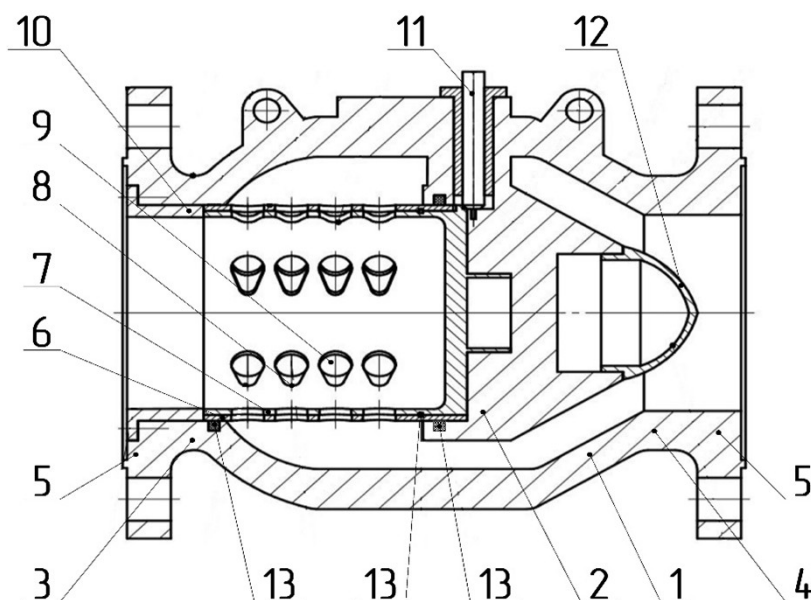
Схема осевого регулирующего клапана с запирающим устройством поворотного типа [xx]: 1 – внешний корпус, 2 – внутренний корпус, 3 – выходной патрубок, 4 – входной патрубок, 5 – фланец, 6 – делитель потока (сепаратор), 7 – запирающий орган, 8 – отверстие криволинейной формы, 9 – отверстия, 10 – расширительная втулка, 11 – вал, 12 – заглушка, 13 – уплотнение
